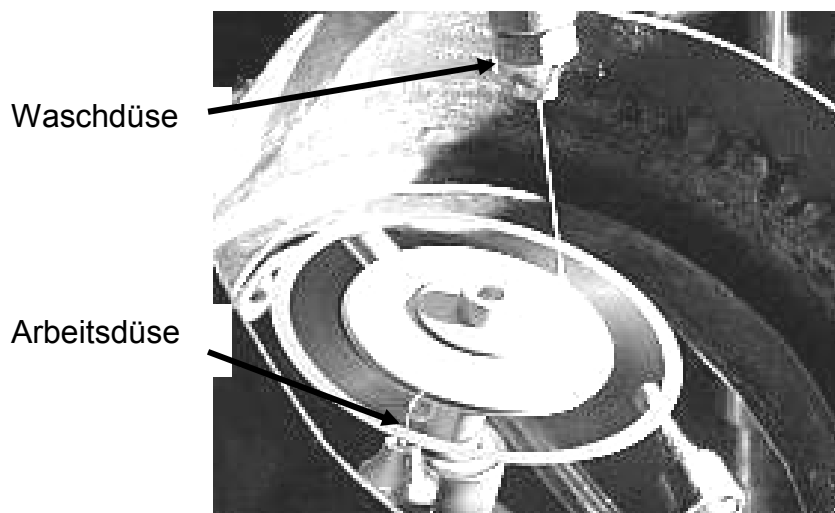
Aufsicht auf das rotierende Schneidwerkzeug mit Fluid- und Reinigungsstrahl
